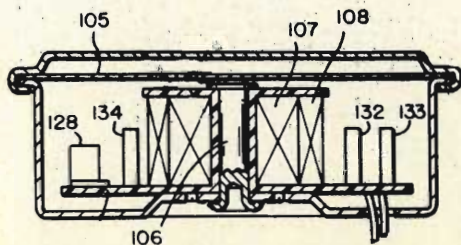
Vista in sezione dell'auricolare con all'interno il piccolo stampato.
